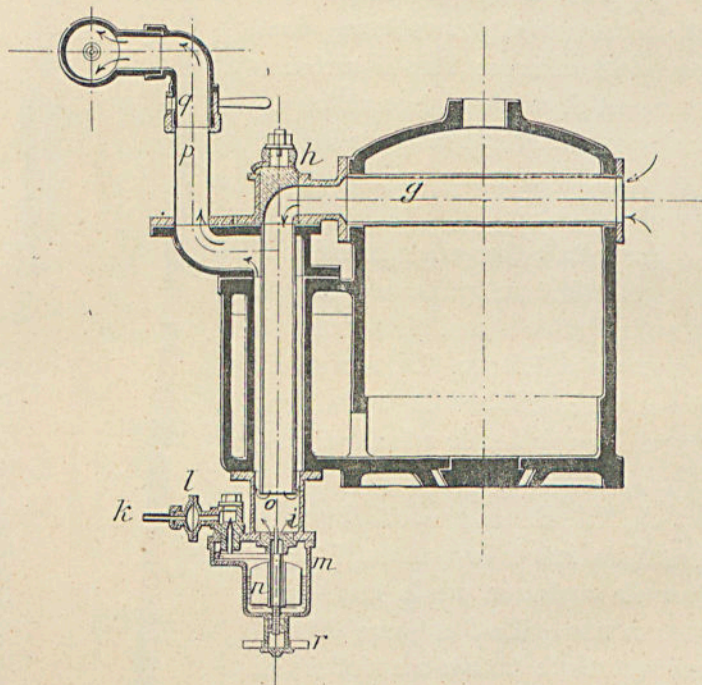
Carburateur à alcool Fritscher et Houdry.
